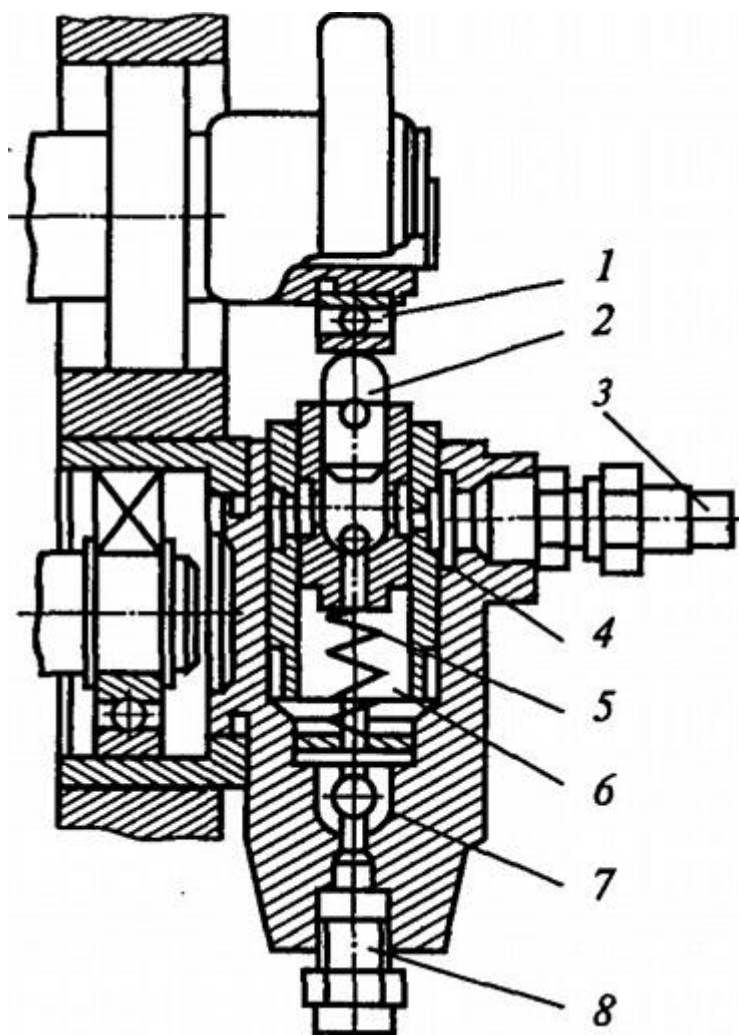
Смазочный насос плунжерного типа:
